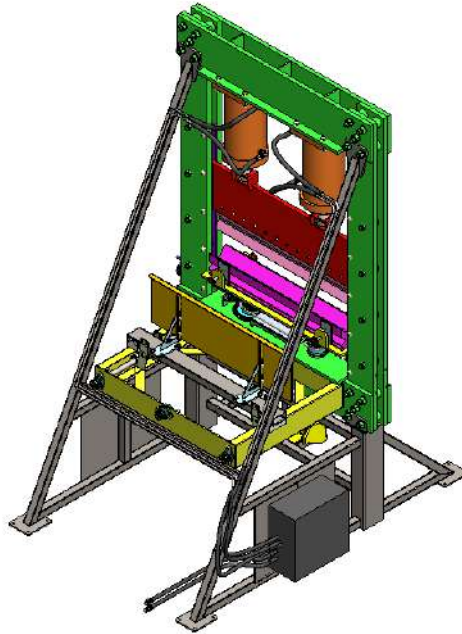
Modelo 3D final de la parte mecánica. Vista isométrica 1.
